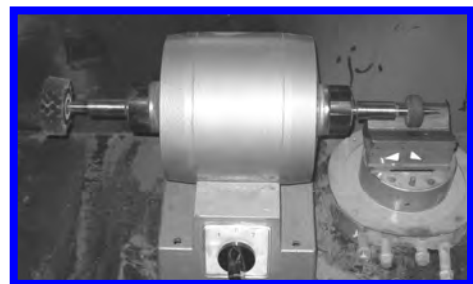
Полировальный станок для обработки изделий с покрытиями
